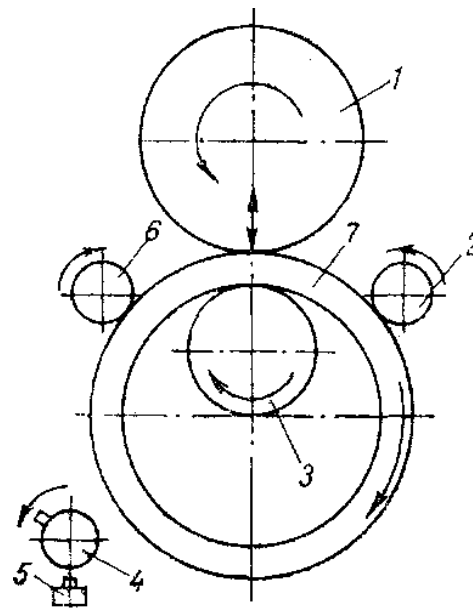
Схема розкатування кільцевих заготовок:
